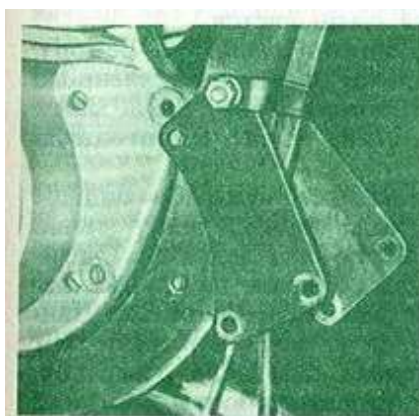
Пластины крепления, повернутые в направлении от двигателя
